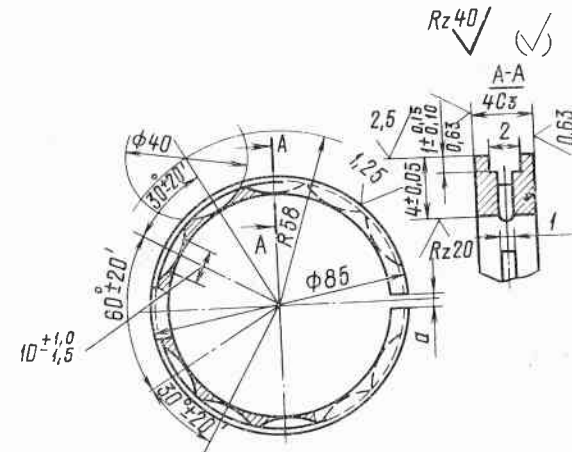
Кольцо маслосъемное 5Д2—24.00.04 Fig. 79. Piston ring, oil-scraper, 5Д2—24.00.04
